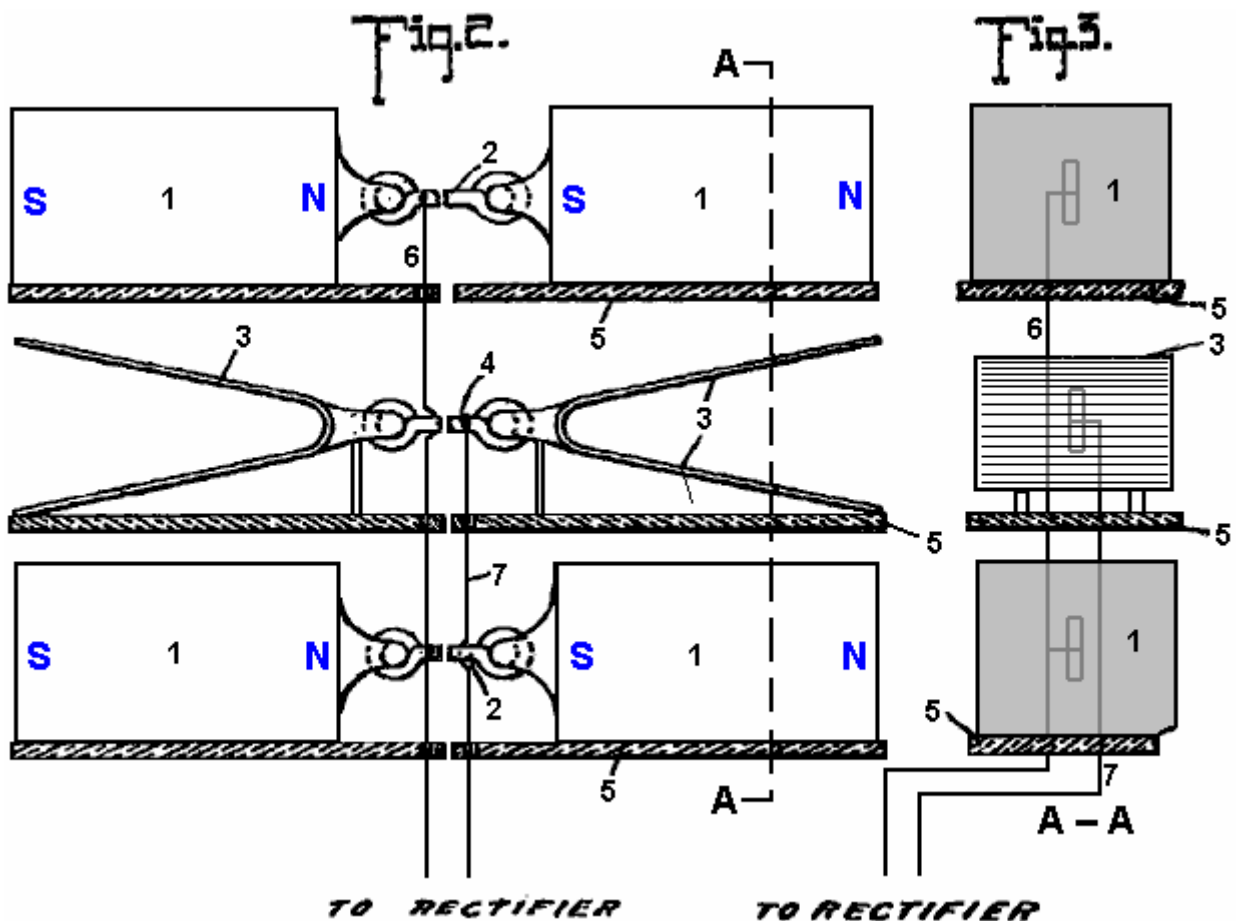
es una vista de elevación de lado de las partes vistas en el plan en Fig.1
